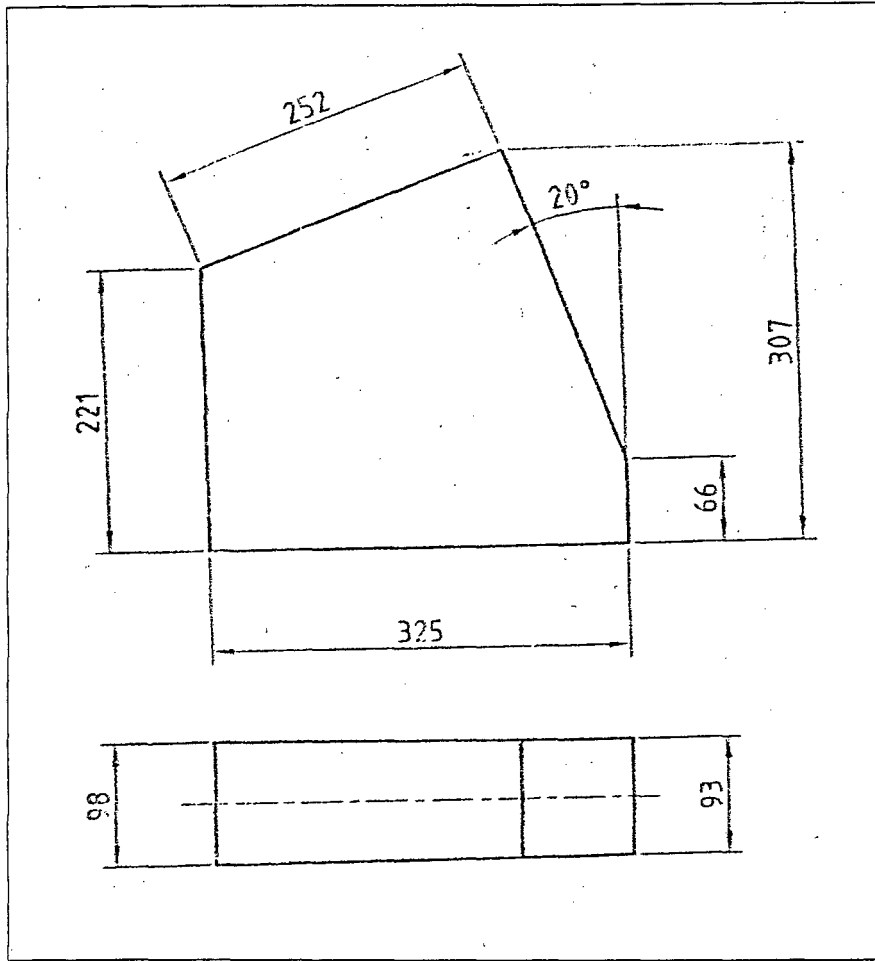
DIMENSIONES DE LADRILLOS BASE TECHO
